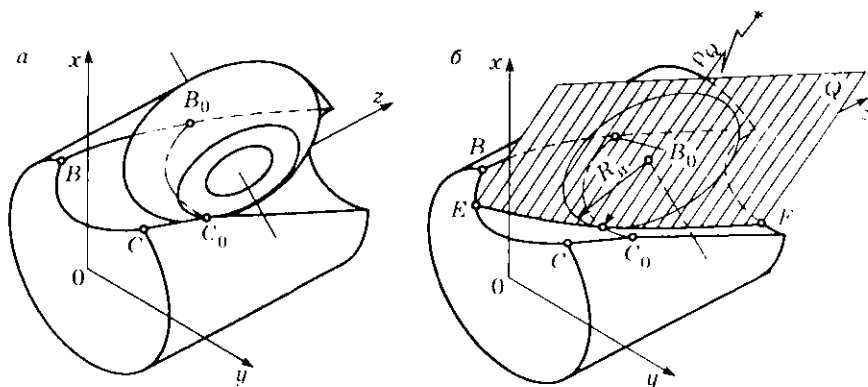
Сопряжение производящей поверхности дисковой фрезы с винтовой поверхностью детали
